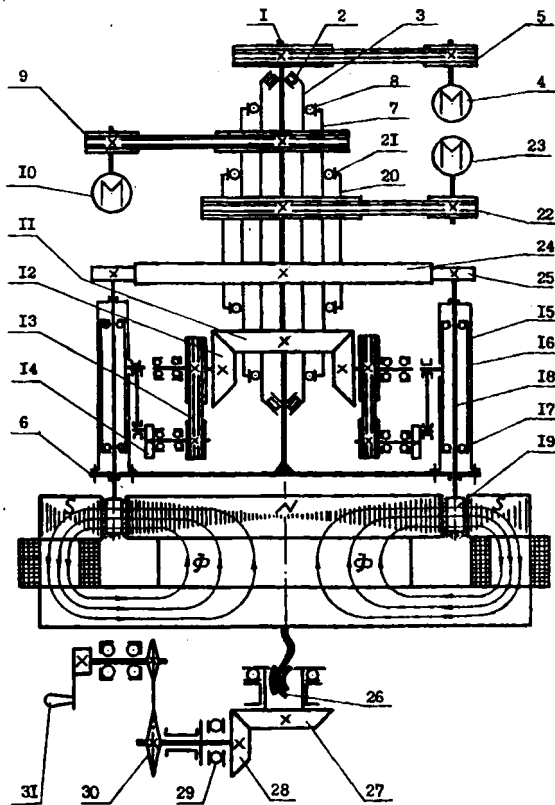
Кинематическая схема магнитно-абразивного роторного станка модели MARC
